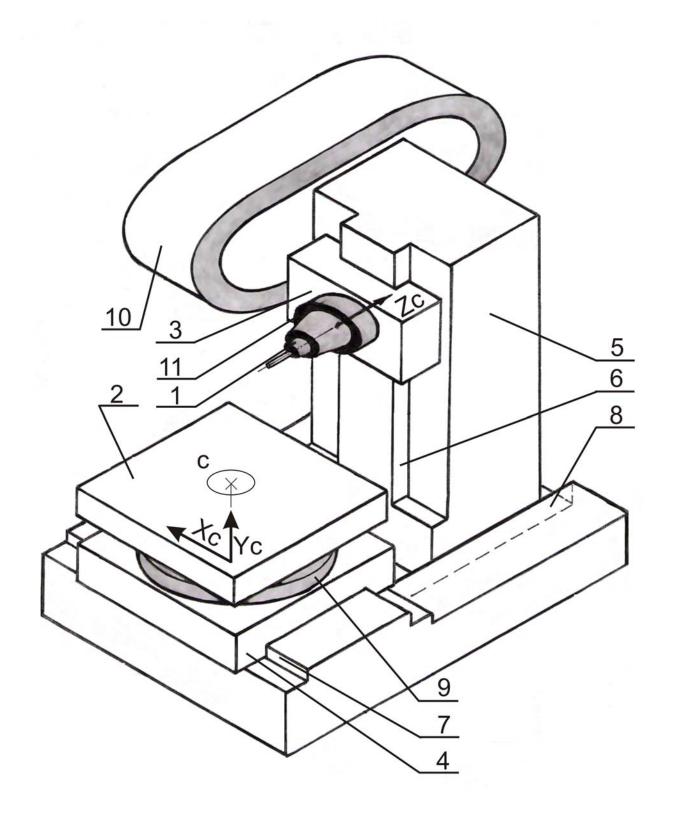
Структурная схема горизонтального ОЦ: 1- шпиндель; 2- рабочий стол; 3,4,5- подвижные элементы; 6,7,8- направляющие; 9- поворотный механизм; 10- инструментальный магазин; 11- телескопическое устройство крепления шпинделя; C- обозначение поворота детали; $X_{\rm c},Y_{\rm c},Z_{\rm c}-$ координатные оси системы координат станка
